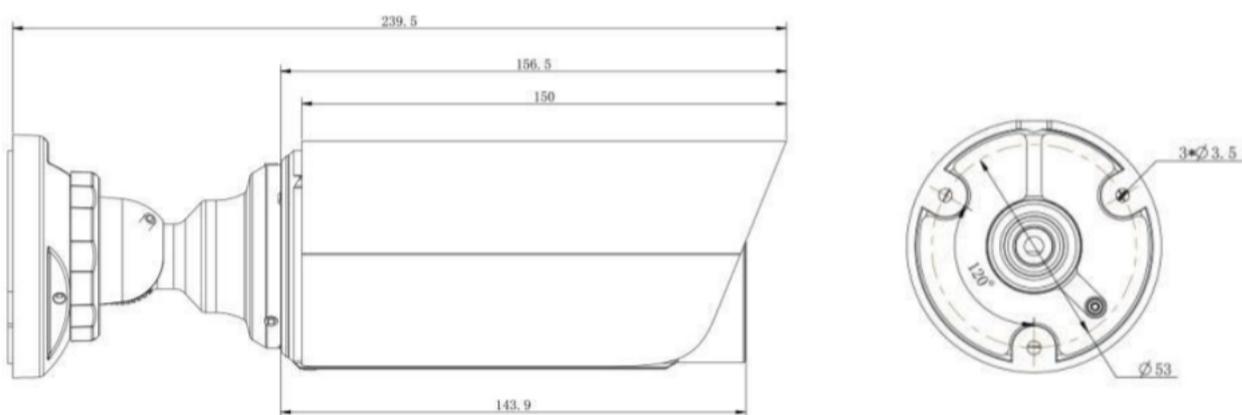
IP-камера VisorJet Smart Bullet mini
